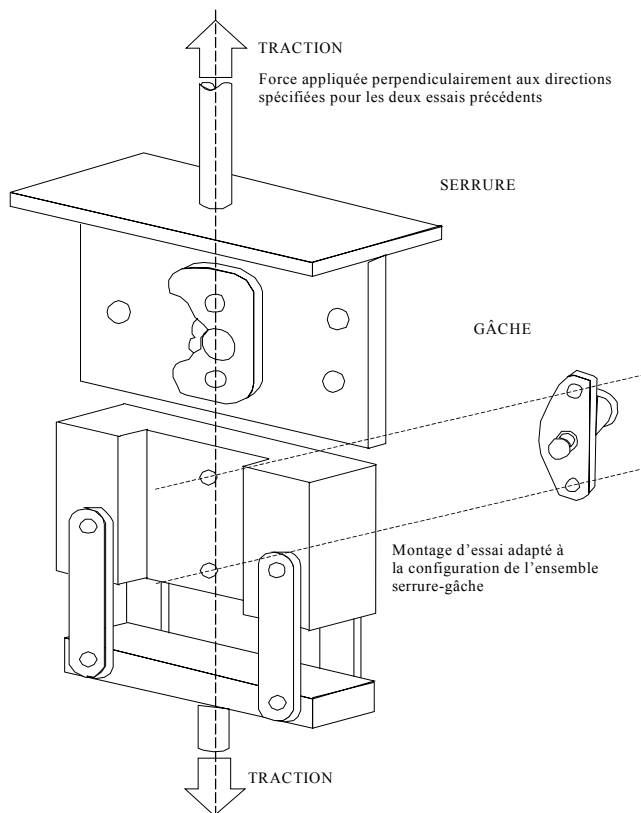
Serrure de porte – Montage pour l'essai n° 3 d'application d'une force (portes arrière seulement)
